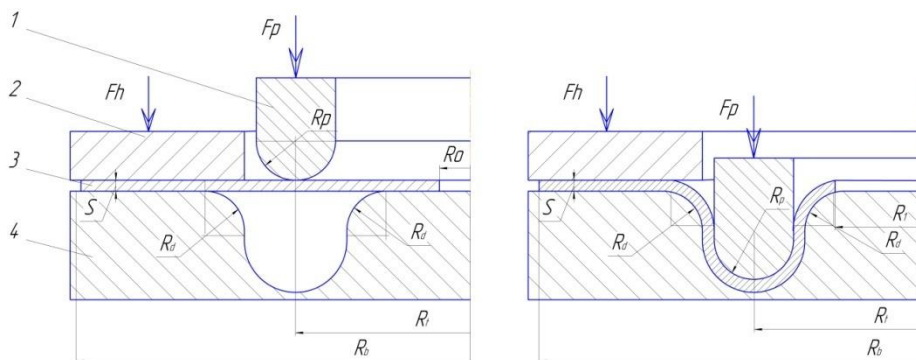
Схемы вытяжки полутора из кольцевой заготовки:
